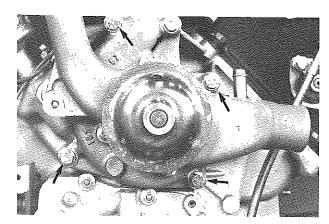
Viti fissaggio pompa acqua Water pump screws
